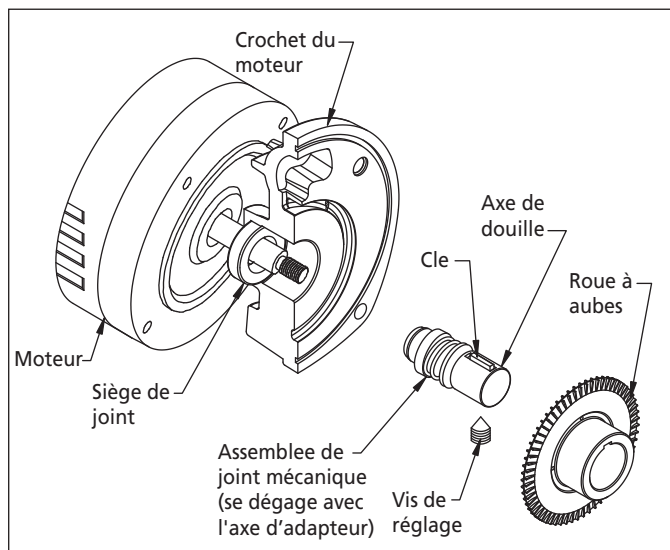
Déplacement de roue à aubes, de douille et d'Assemblée
